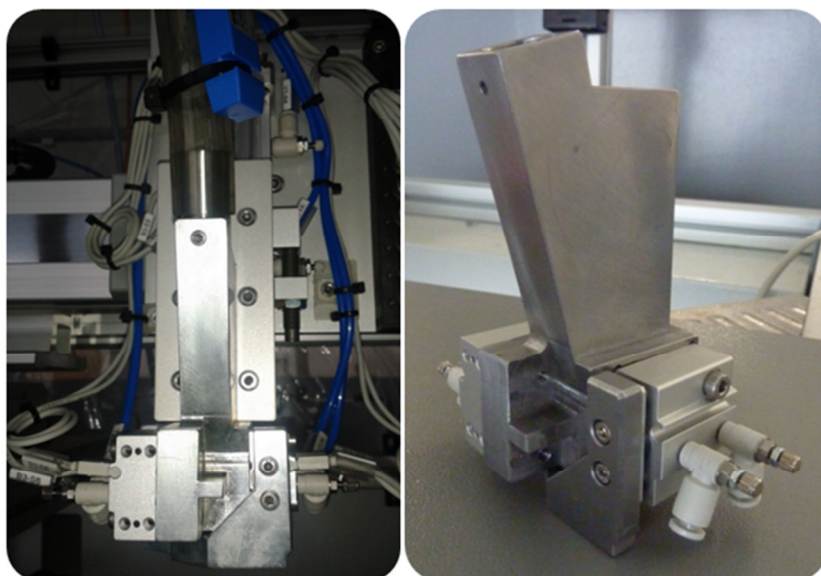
Detalhe do *Nozzle* [fotos da máquina]
